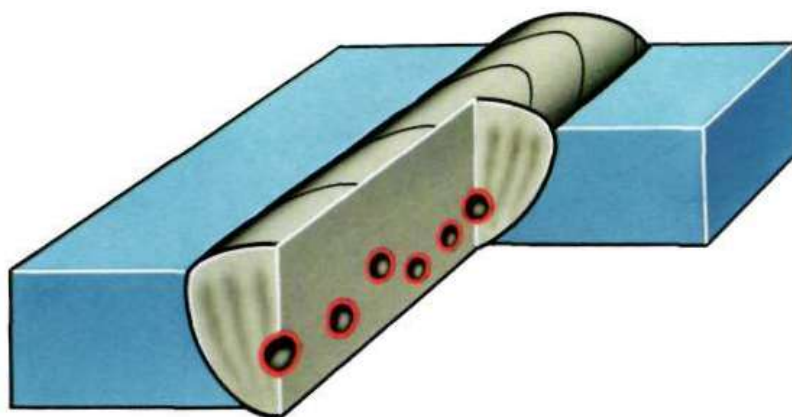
Дефекты сварного шва по типу цепочки пор
